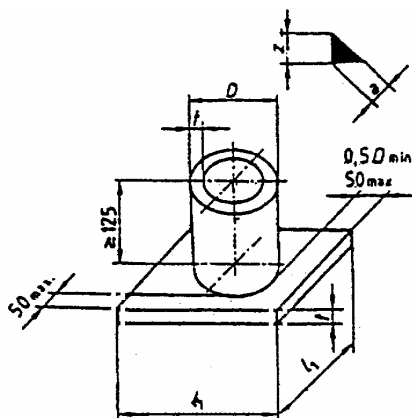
Dimensiunile probei pentru sudură în colț la țeavă
